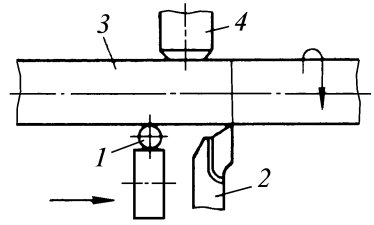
Схема одновременного точения и обкатывания при установке шарика за резцом:
